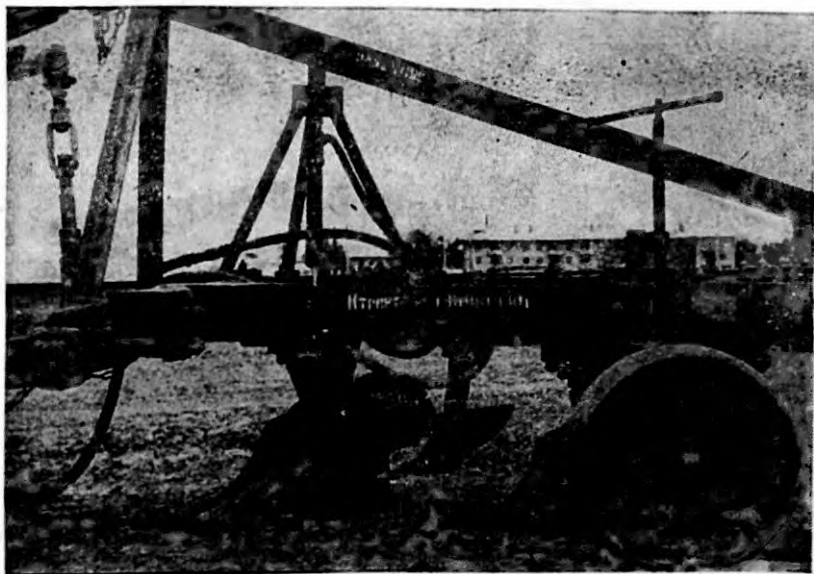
Установка левооборачивающего корпуса рядом с первым корпусом плуга ПЛН-5-35.
